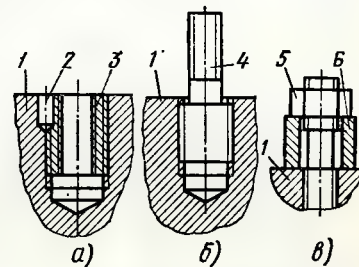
Восстановление резьбовых соединений установкой футорки (а), ступенчатой шпильки (б), шпильки на клее (в)
